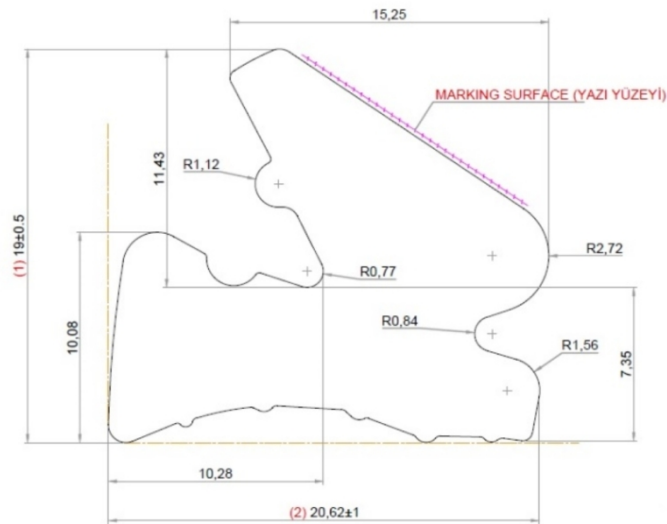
Caractéristiques dimensionnelles du joint élastomère en EPDM S19 Spigot Seal
